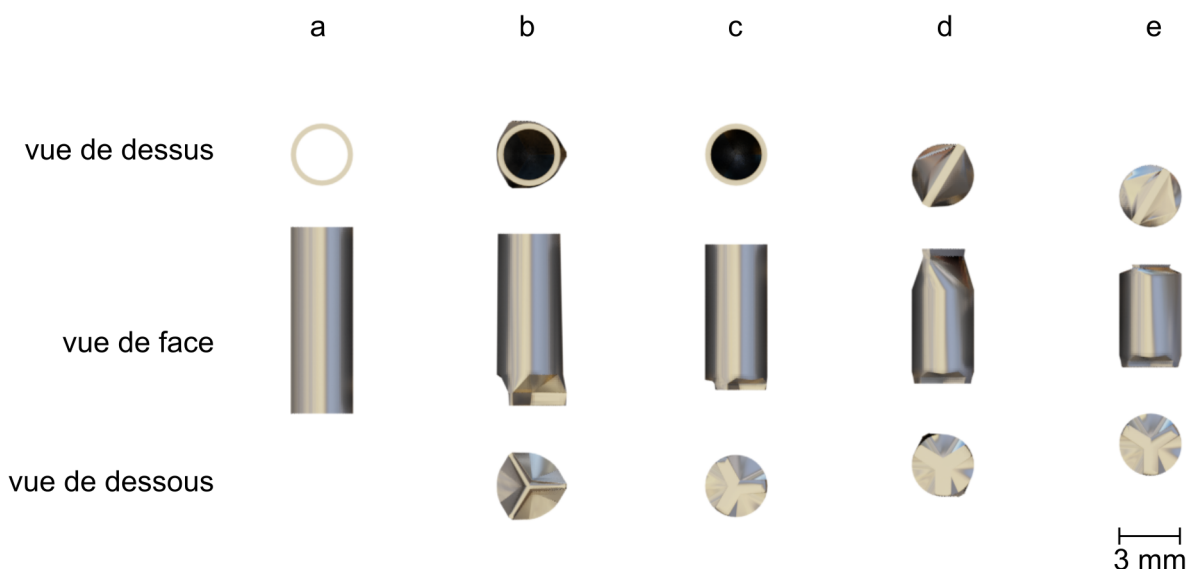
Aspect de la capsule tout au long de sa mise en forme. a. tube de Pt de 9 mm de haut découpé d'un tube plus grand, b. tube plié en forme d'étoile à trois branches en une extrémité, c. étoile à trois branche soudée et emboutie, d. capsule chargée de poudre de réactif solide et de gaz soudée en sa deuxième extrémité et e. capsule chargée et étanche, écrasée, prête à introduire dans l'assemblage.
